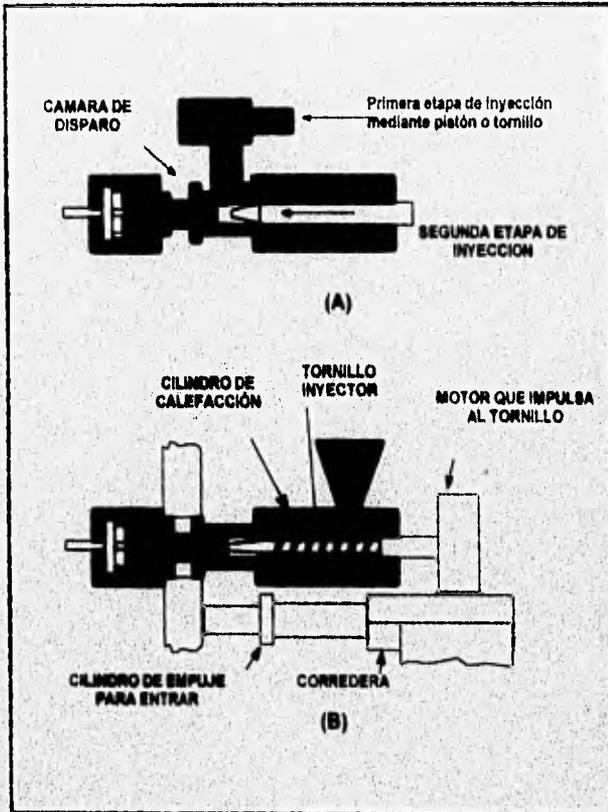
SISTEMAS DE MOLDEO POR INYECCIÓN
